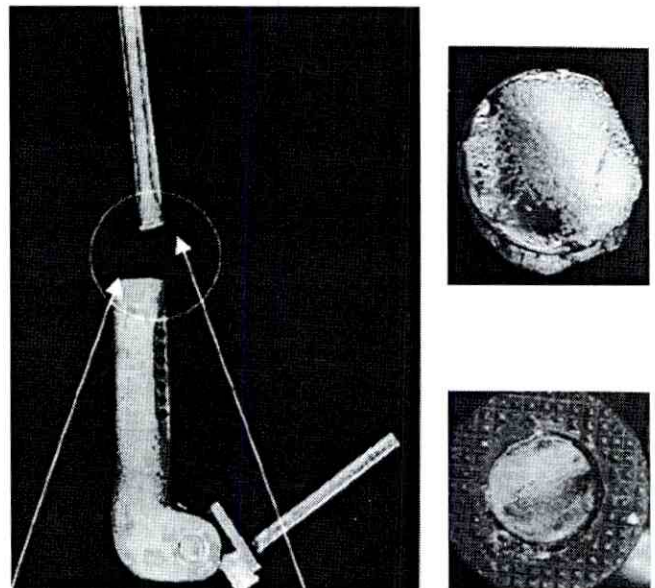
Aspecto general de la prótesis fracturada. Nótese que la fractura se produce en un cambio brusco de sección.
